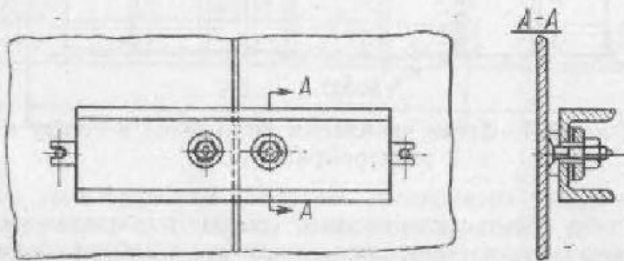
Приспособление для обратного выгиба кромок обшивки.
